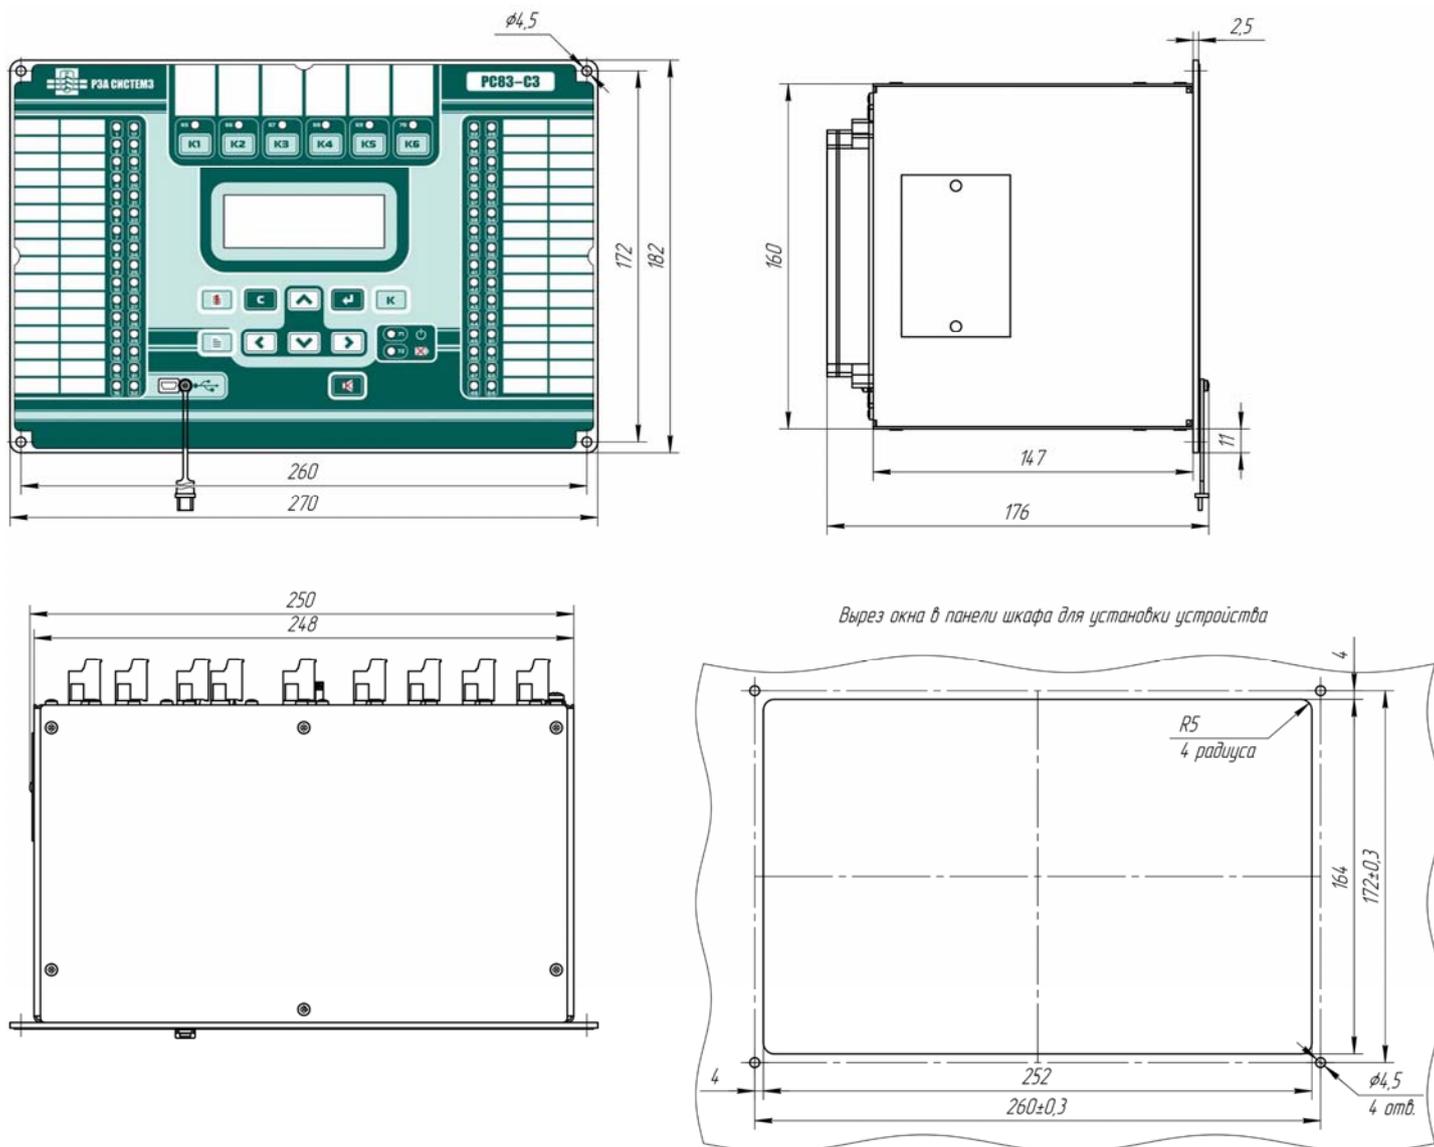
Габаритные и присоединительные размеры устройства РС83-С3
